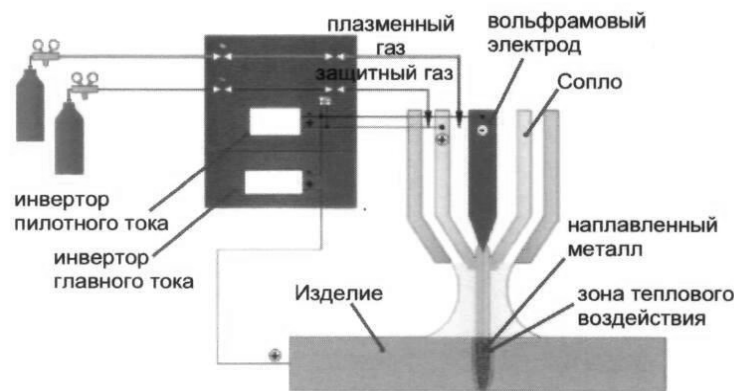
Схема процесса плазменно-дуговой шовной сварки.
